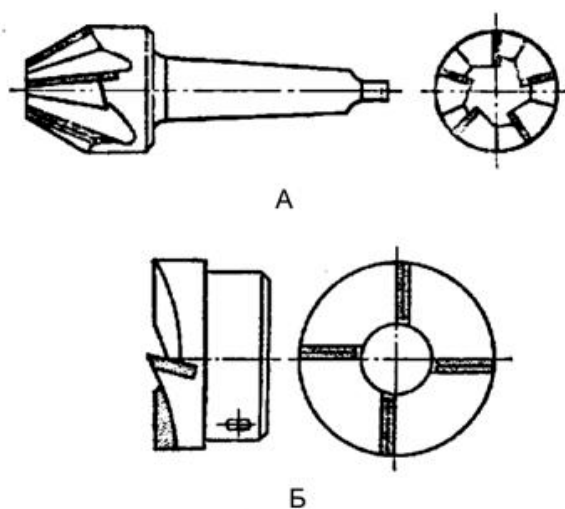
Конический зенкер (зенковка) — А; торцевой зенкер — Б
